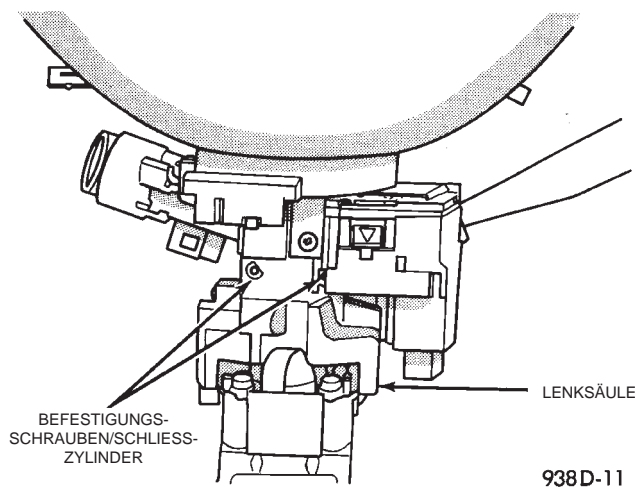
Befestigungsschrauben des Schließzylindergehäuses
